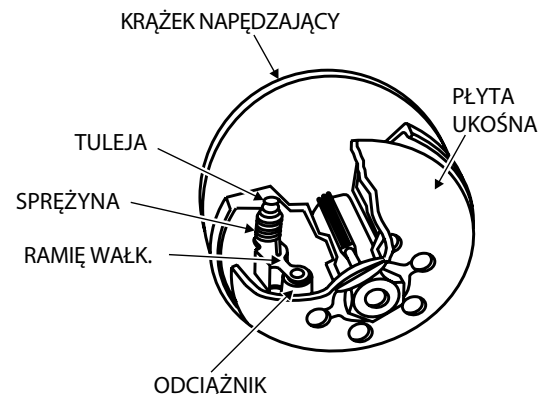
Przełącznik mom. obrotowego (Napędzany odśrodkowo)
